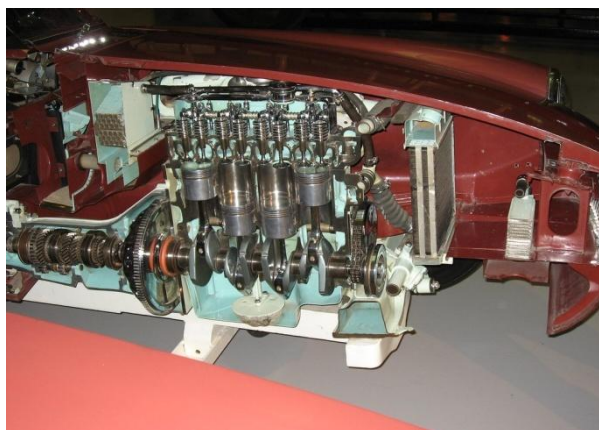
Разрез рядного четырехцилиндрового двигателя
